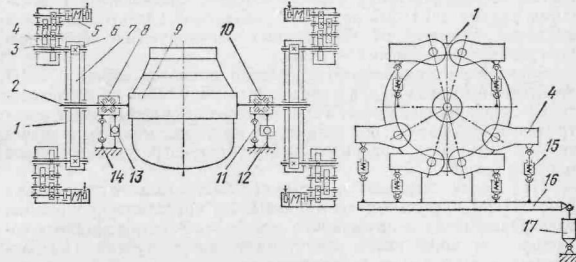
Кинематическая схема механизма поворота с двусторонним приводом, системы фиксации тихоходного и быстроходных редукторов и опор конвертера вместимостью 350—400 т
